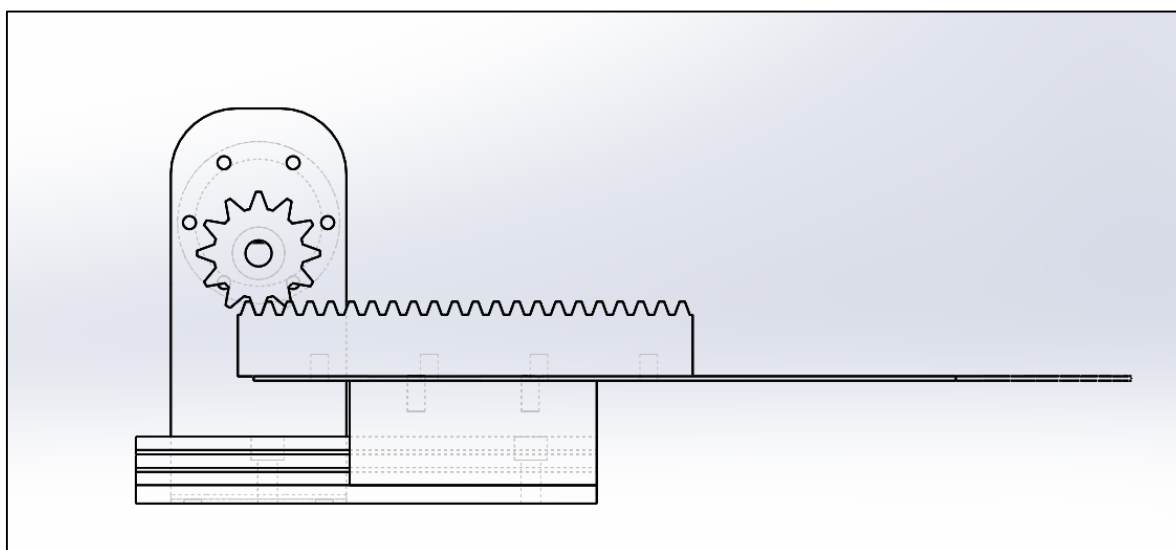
Vista frontal do mecanismo dispenser de pipoca.
